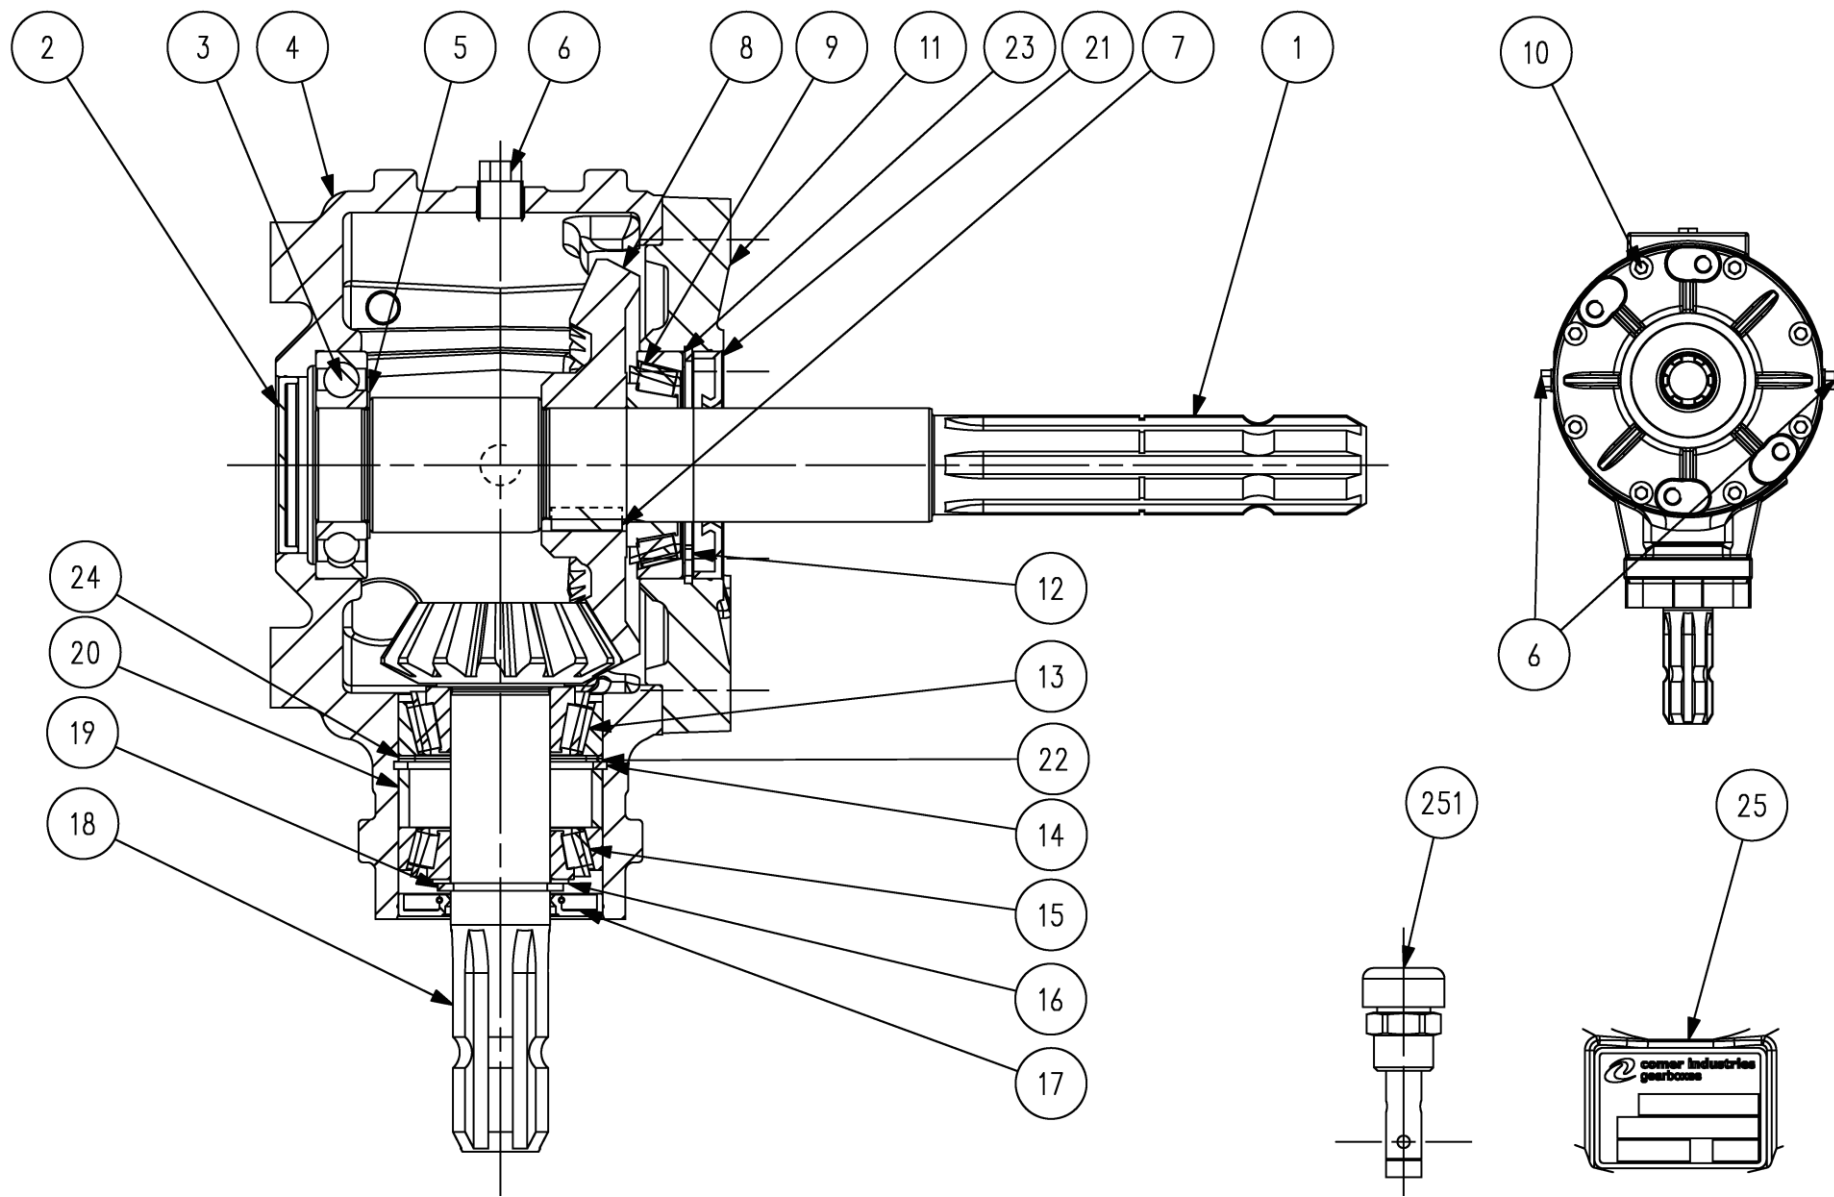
Редуктор 9.304.528.00 "Comer industries"
